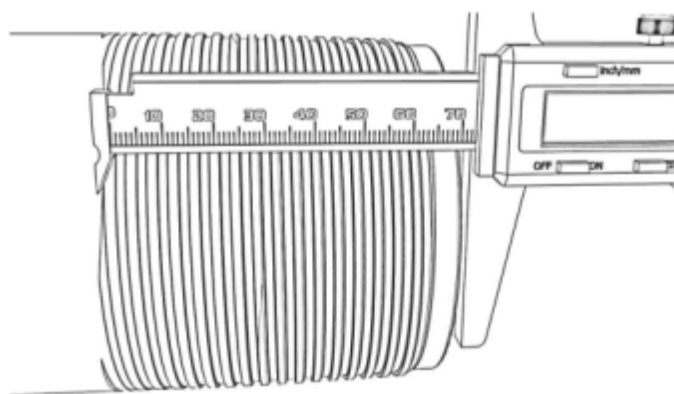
Измерение длины резьбы при помощи штангенглубиномера
